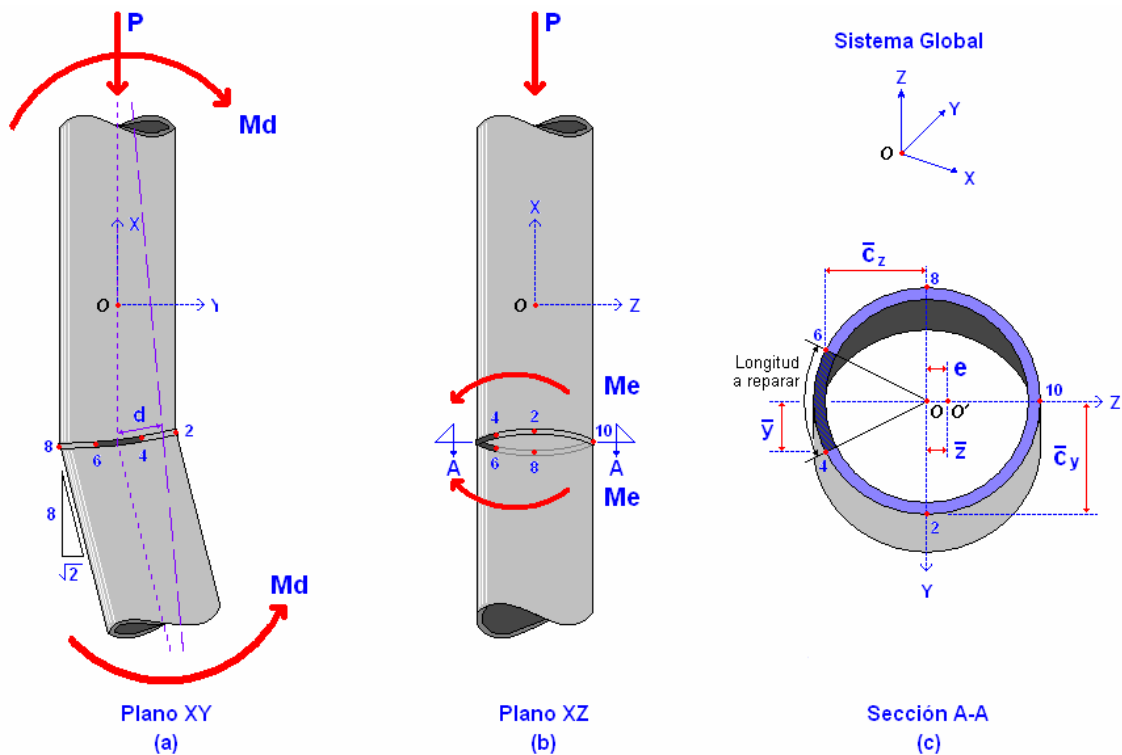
Reparación de soldadura en la parte lateral.
